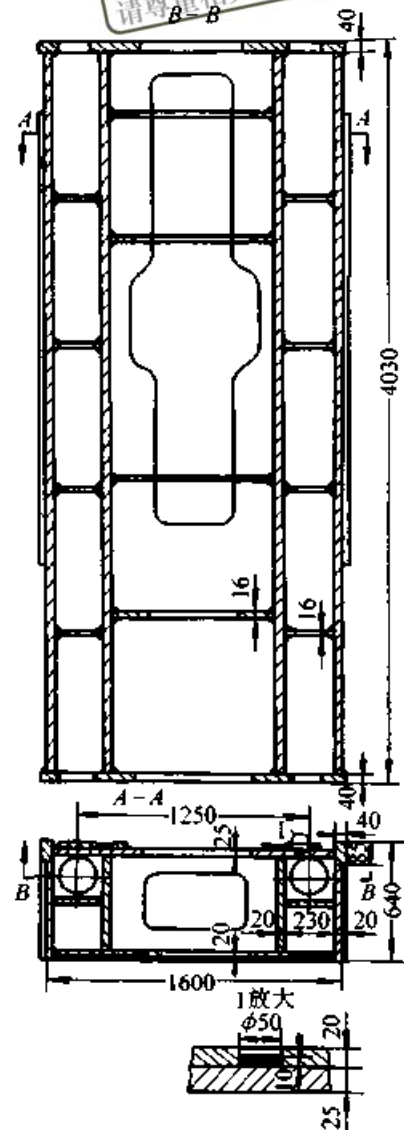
JD36-400 型机械压力机焊接立柱
